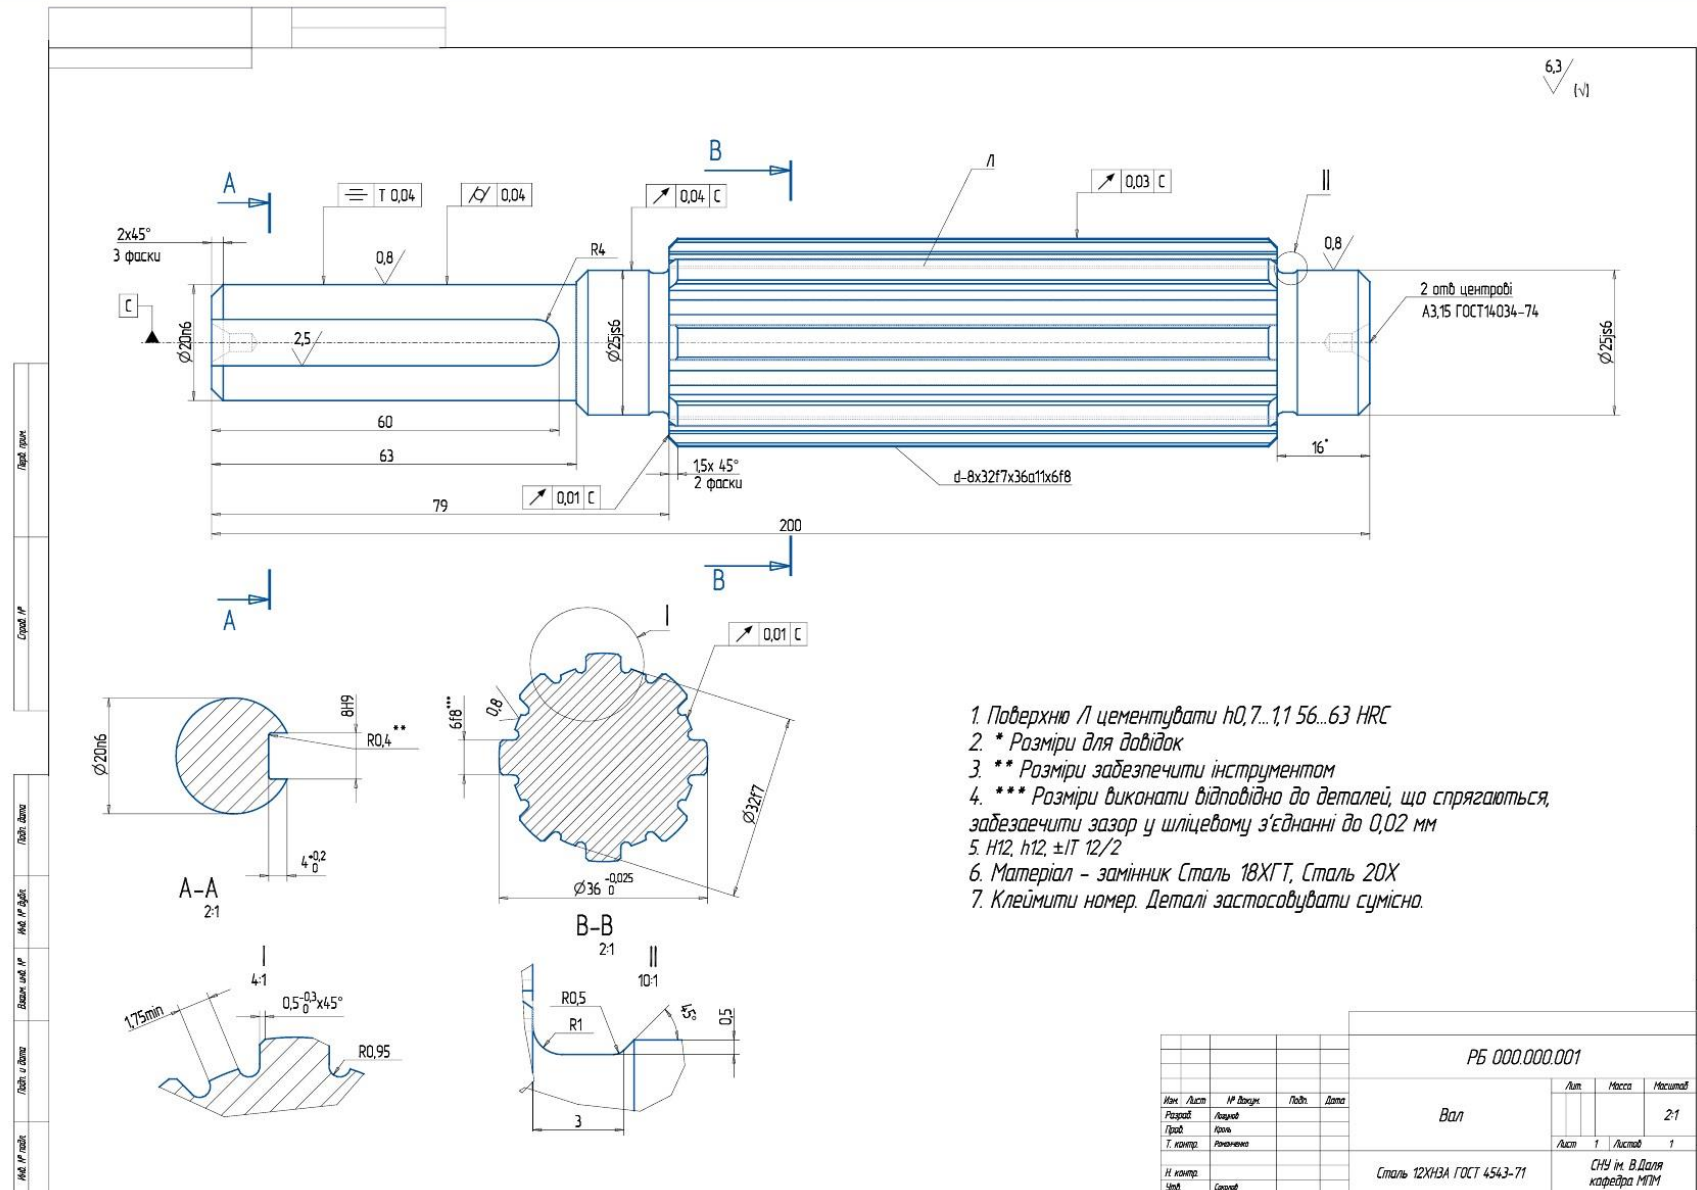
Кресленик деталі «Вал шліцьовий»
